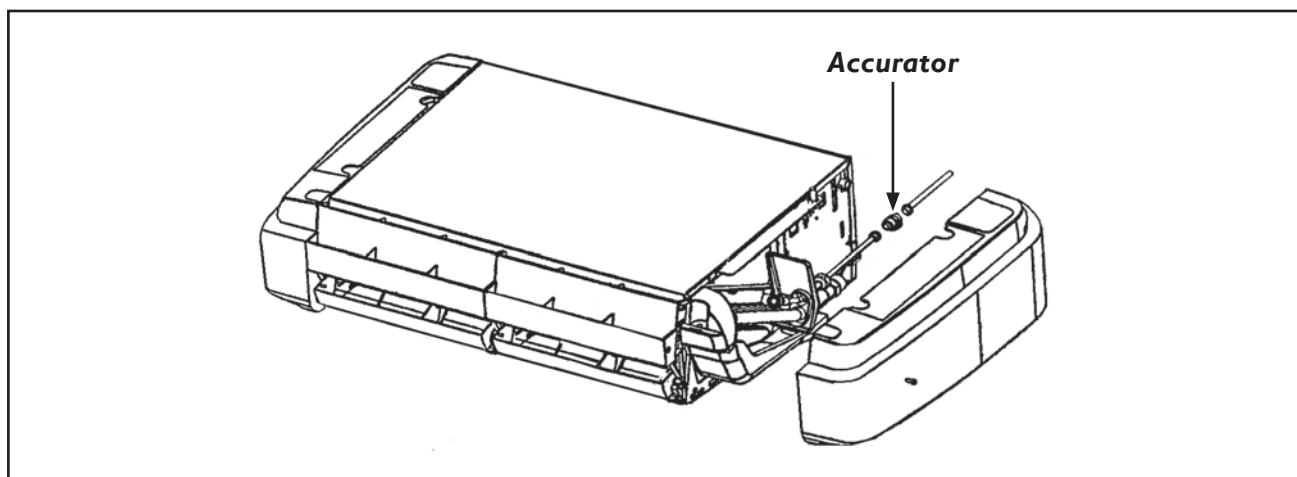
INSTALAÇÃO DO KIT SISTEMA DE EXPANSÃO
